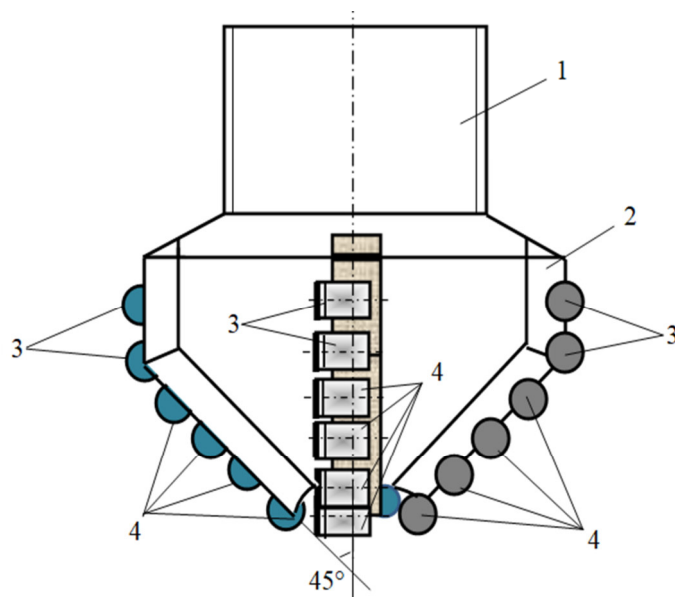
Долото с вращающимися резцами *PDC*: 1 – корпус с резьбой; 2 – матрица; 3 и 4 – вращающиеся резцы
